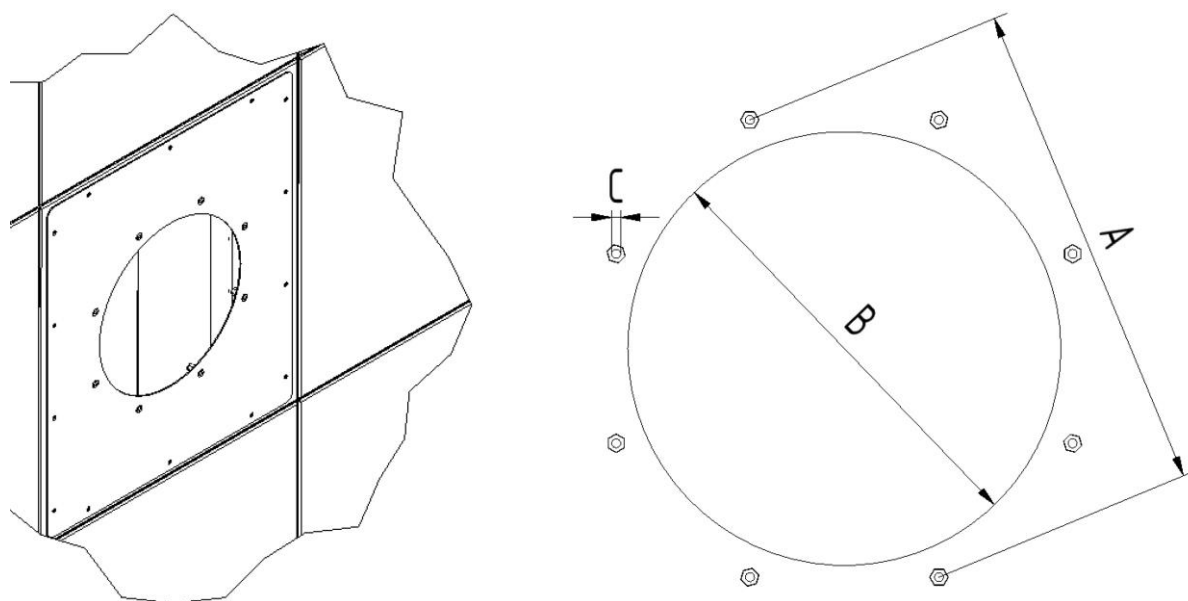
Габаритный чертеж – присоединение системы трубопроводов
